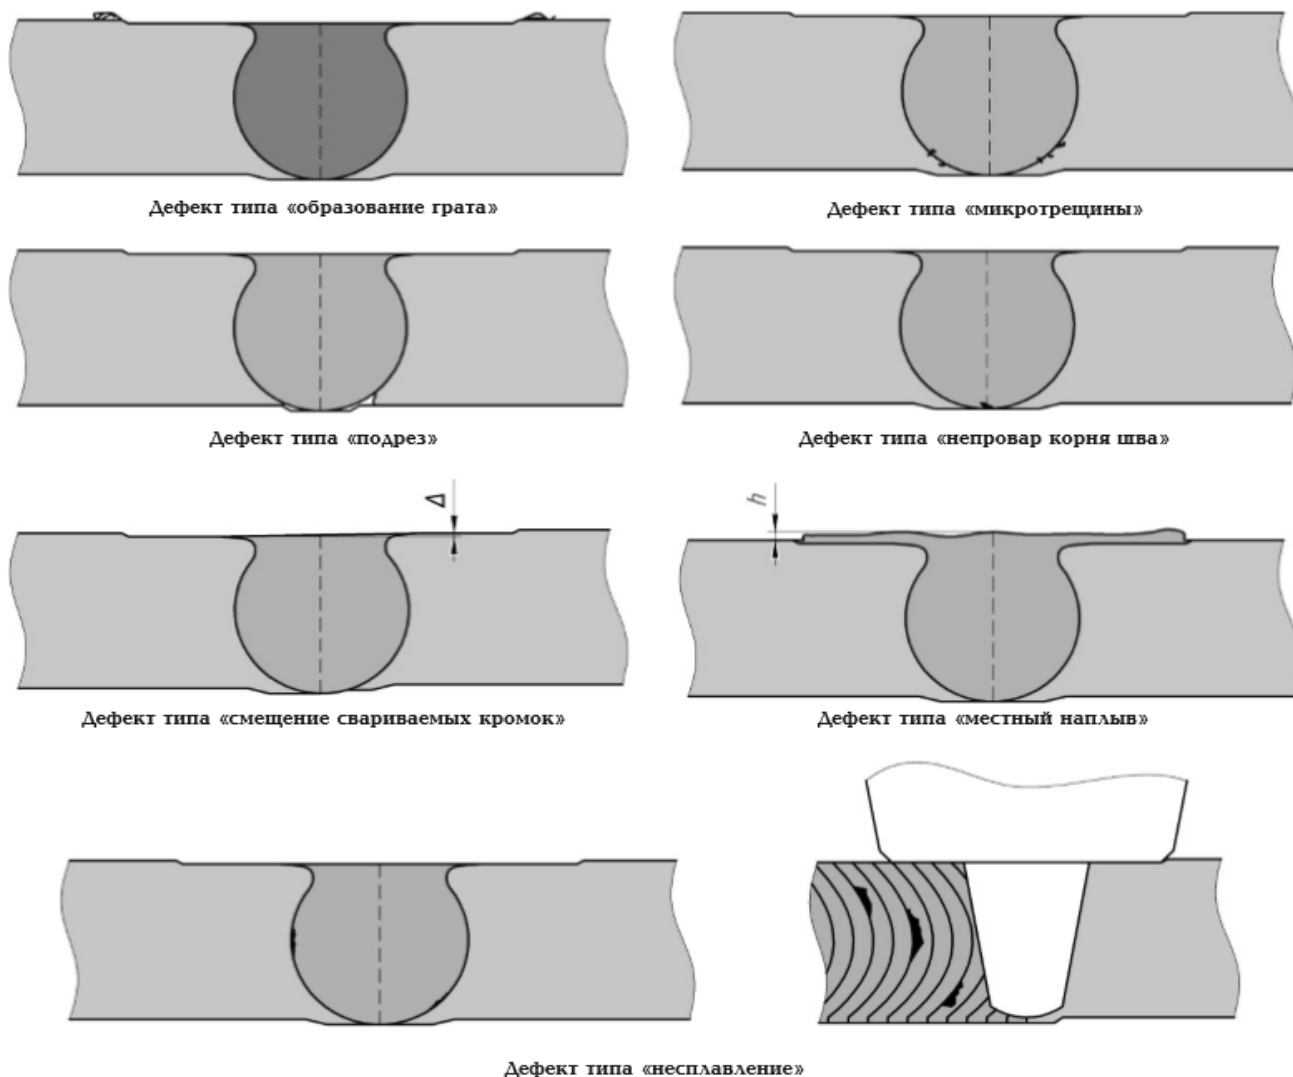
Типы дефектов, характерные для сварки трением с перемешиванием [3]
